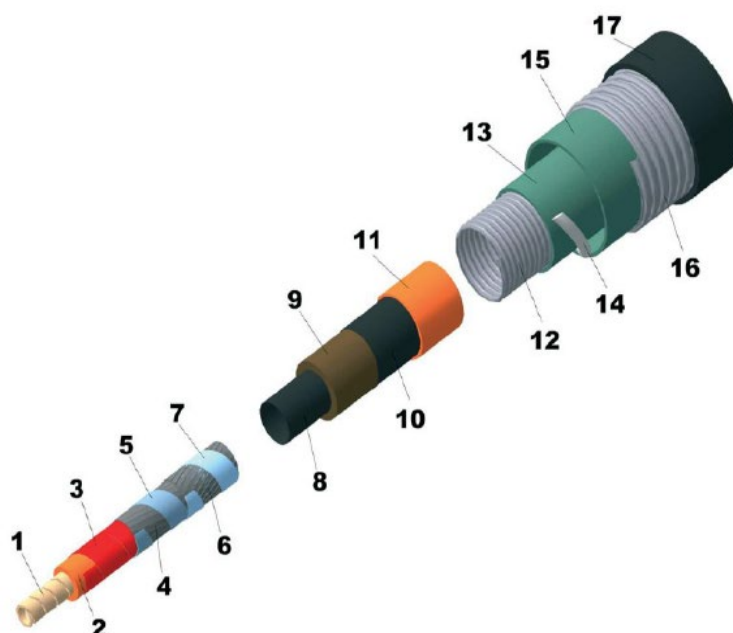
Конструкция сверхпроводящего силового кабеля:
